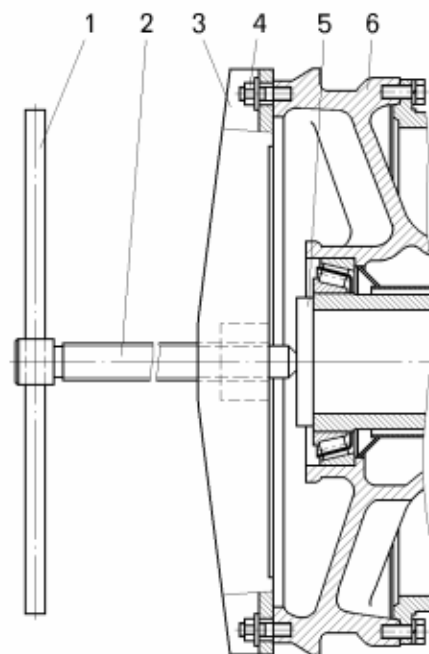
Приспособление для съема внутреннего кольца внутреннего подшипника 2007164А вместе с крышкой:
